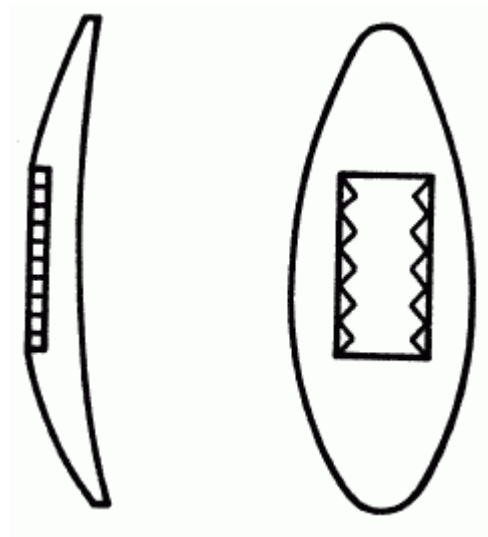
Холодная запрессовка (вставка) одного металла в заготовку блесны другого
